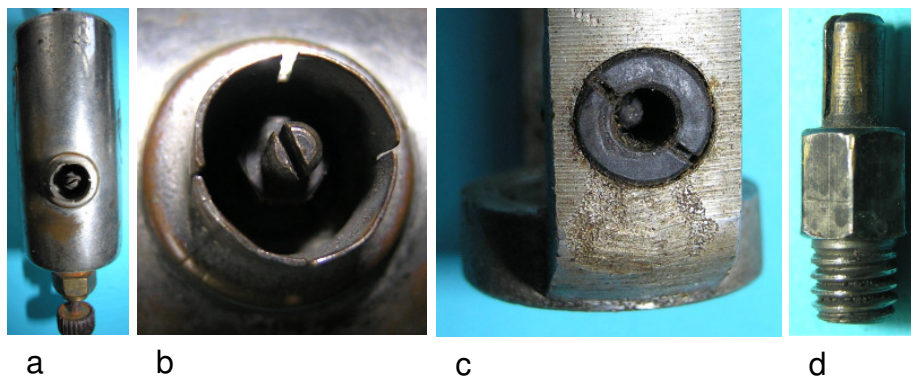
Spannung führender Kontakt: a) Gehäuse mit Kabelanschluss, b) Kabelanschluss, c) Rahmen mit Isolierteil für den Bürstenhalter, d) Einschraubbarer Bürstenhalter mit Stecker
